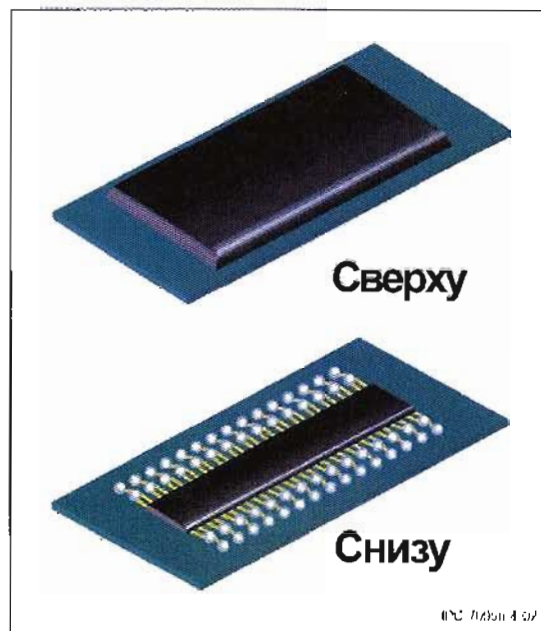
Верхняя часть корпуса BGA BOC-типа, залитого пластиком
